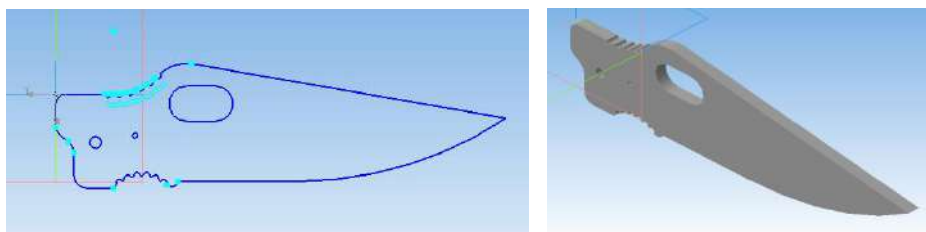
Эскиз и трехмерная модель заготовки клинка
